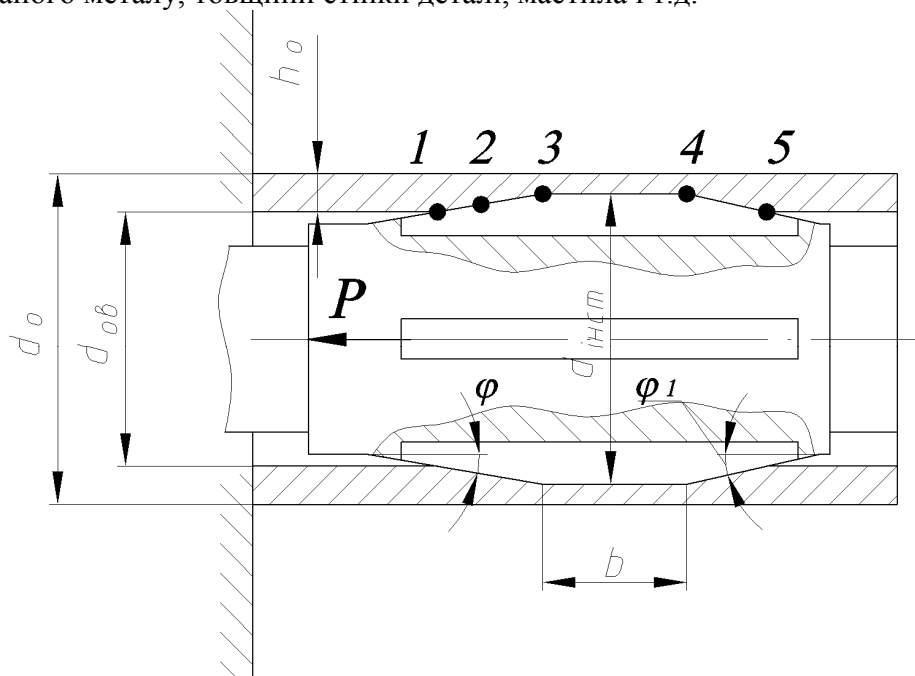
Розрахункова схема калібрування шліцевого отвору
